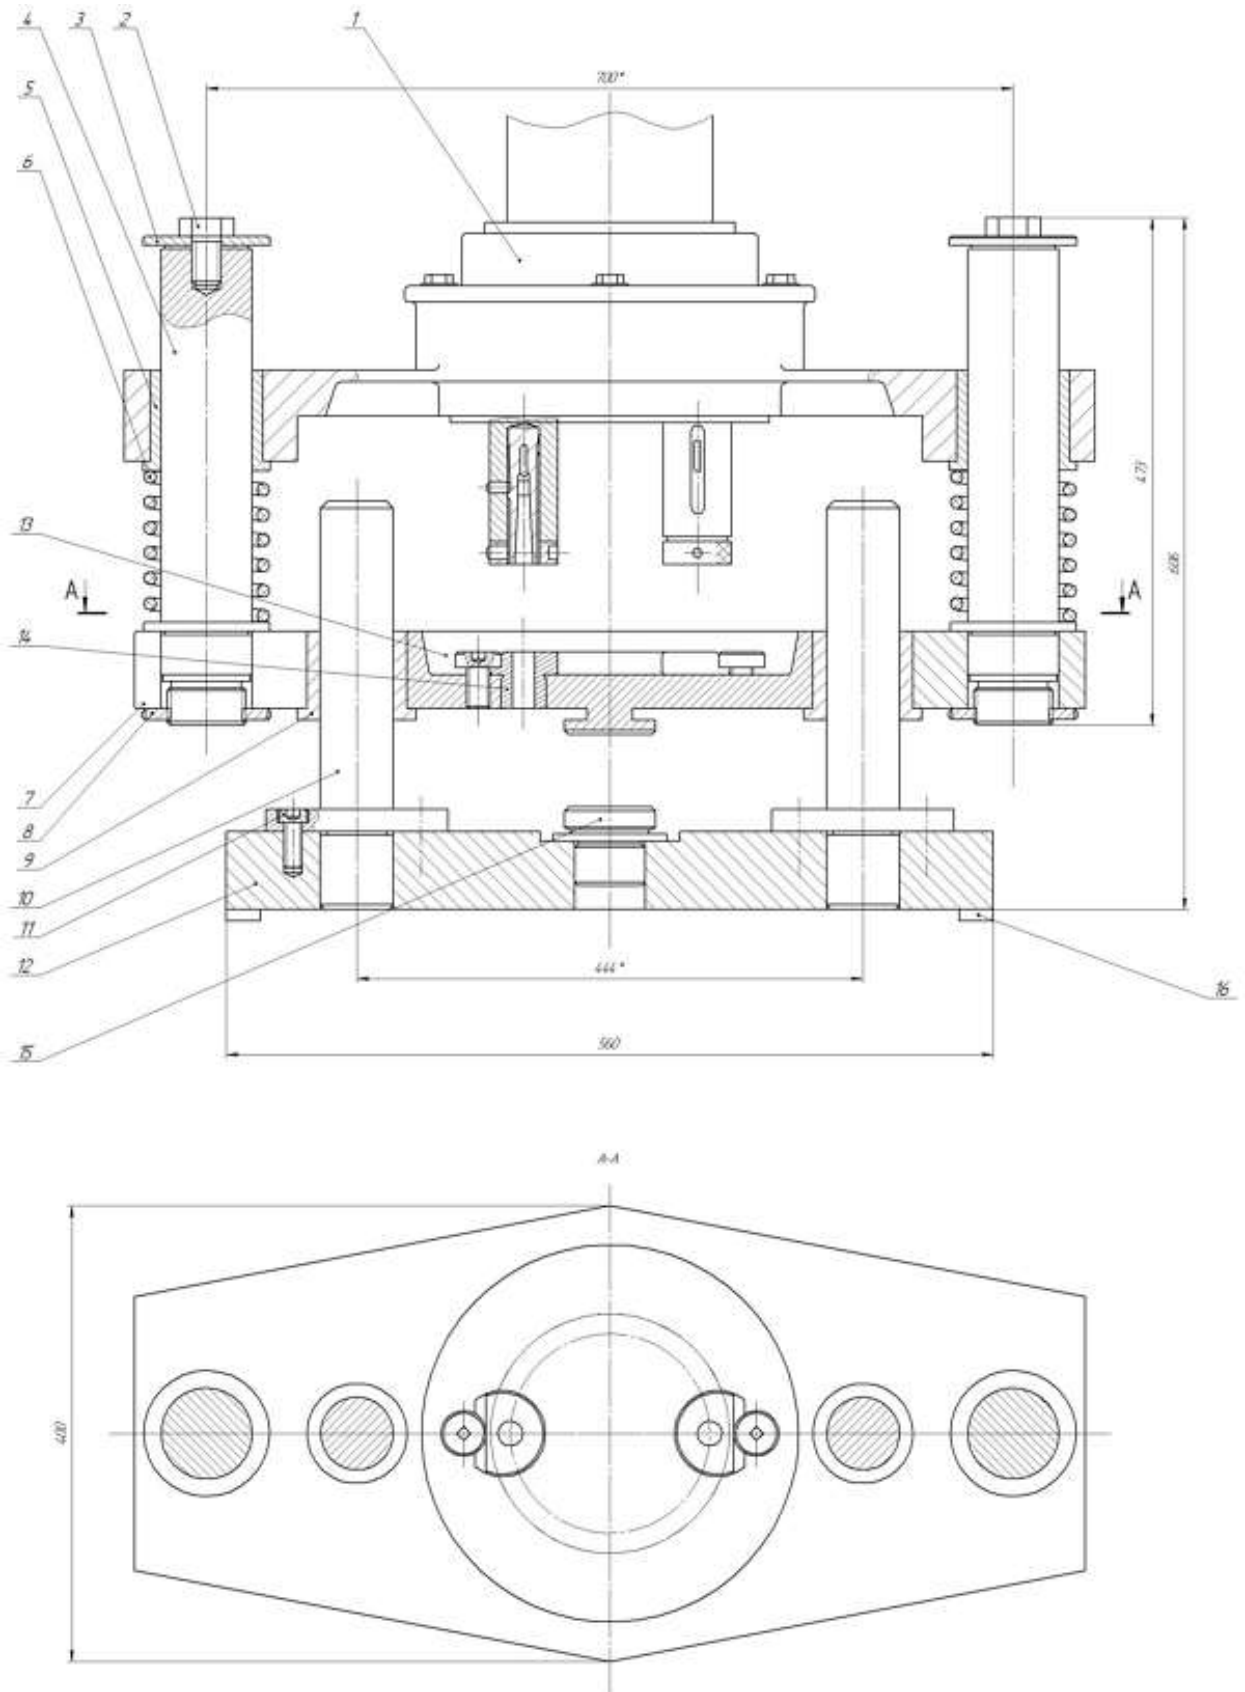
Конструкція кондуктора з двошпindelною головкою
